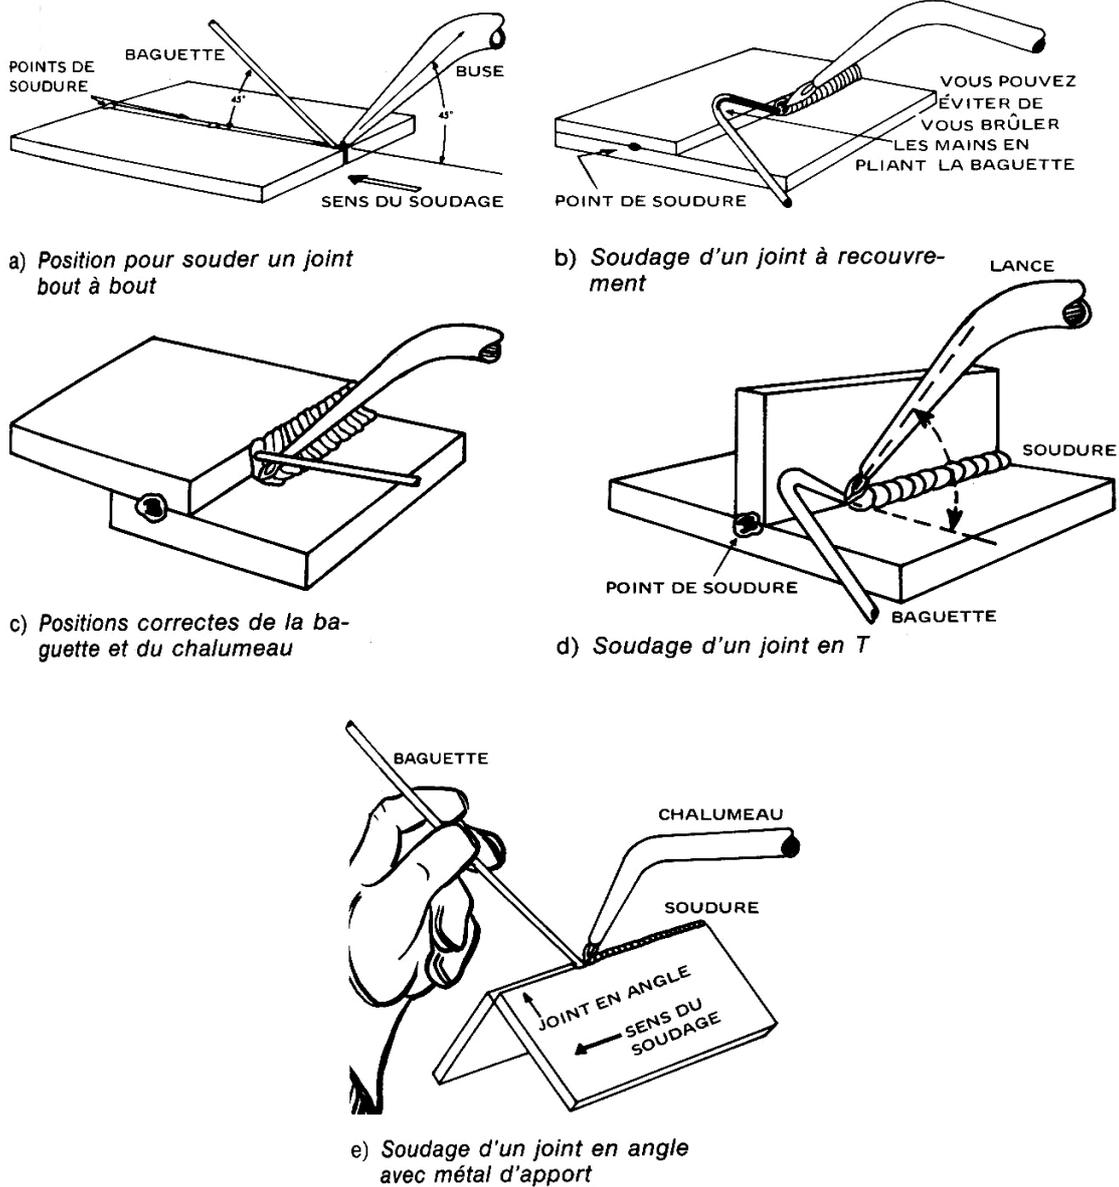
Positions de soudage pour les divers types d'assemblage
